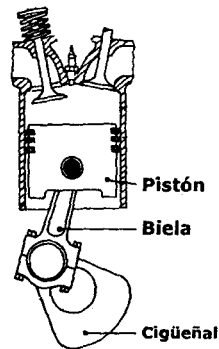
Conjunto pistón-biela-cigüeñal.
